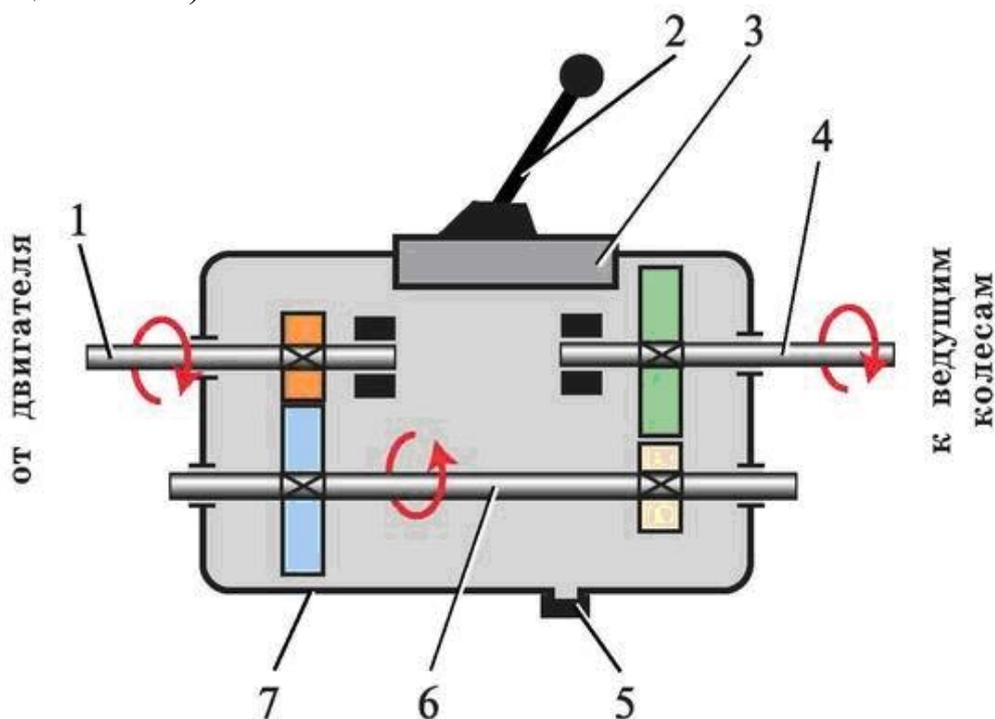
Схема работы коробки передач: 1 - первичный вал; 2 - рычаг переключения передач 3 - механизм переключения передач 4 - вторичный вал; 5 - сливная пробка; 6 - промежуточный вал; 7 - картер коробки передач
